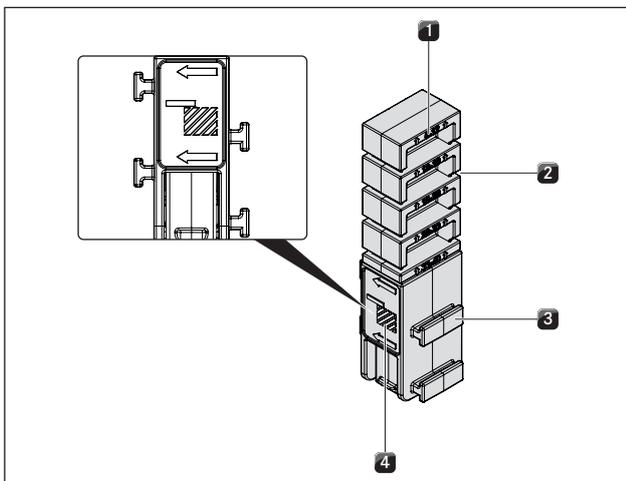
Borna de montaje lado izquierdo (superposición)
